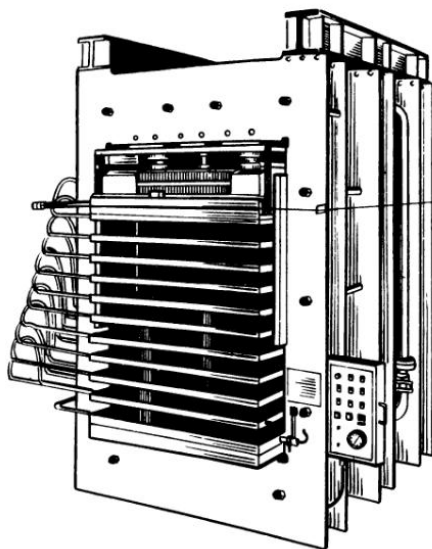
Гидравлический многостажный пресс с обогреваемыми плитами
